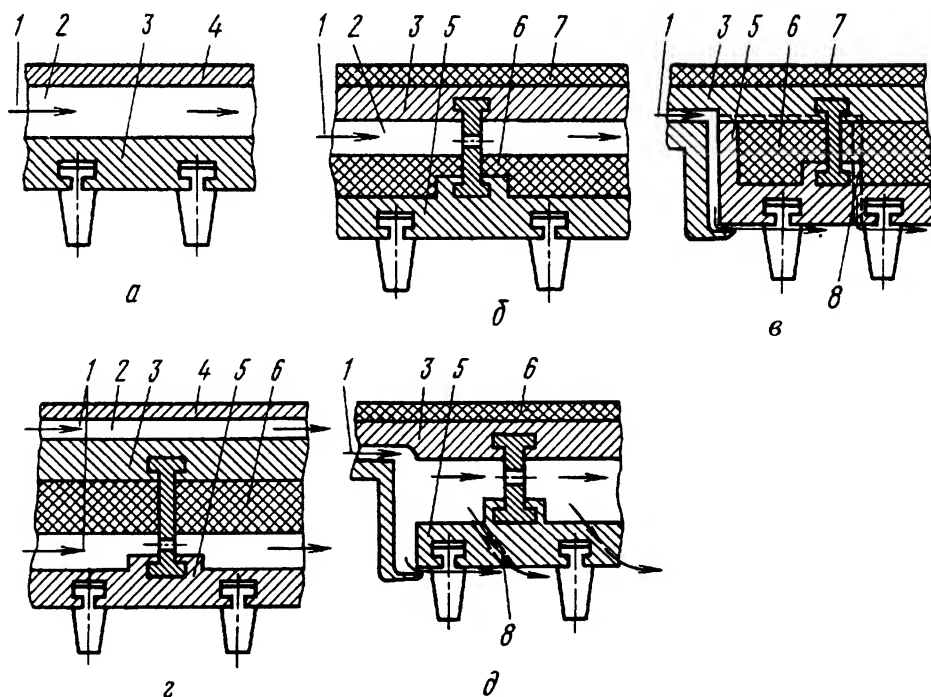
Схемы охлаждения корпусов газовых турбин:
